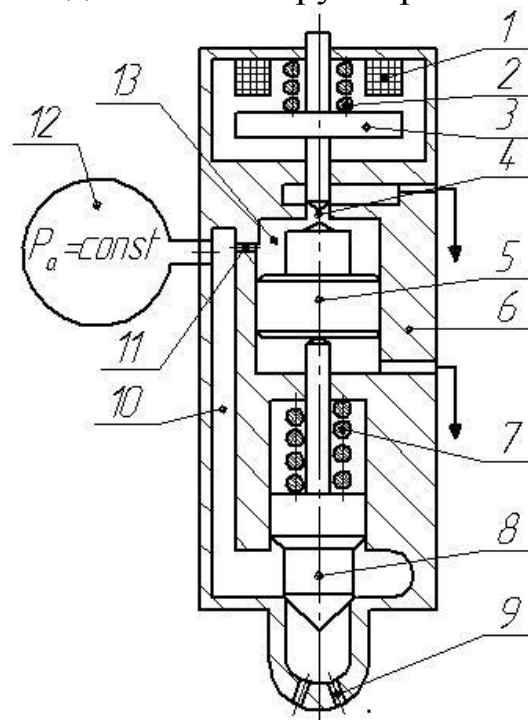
Схема форсунки с электромагнитным управлением: 1 – электромагнит; 2, 7 – пружины; 3 – якорь с уплотняющим конусом; 4 – отсечное калиброванное отверстие (жиклёр); 5 – поршень; 6 – корпус форсунки; 8 – игла распылителя; 9 – сопловые отверстия; 10 – подводящий калиброванный канал (жиклёр); 11 – впускное отверстие; 12 – аккумулятор
